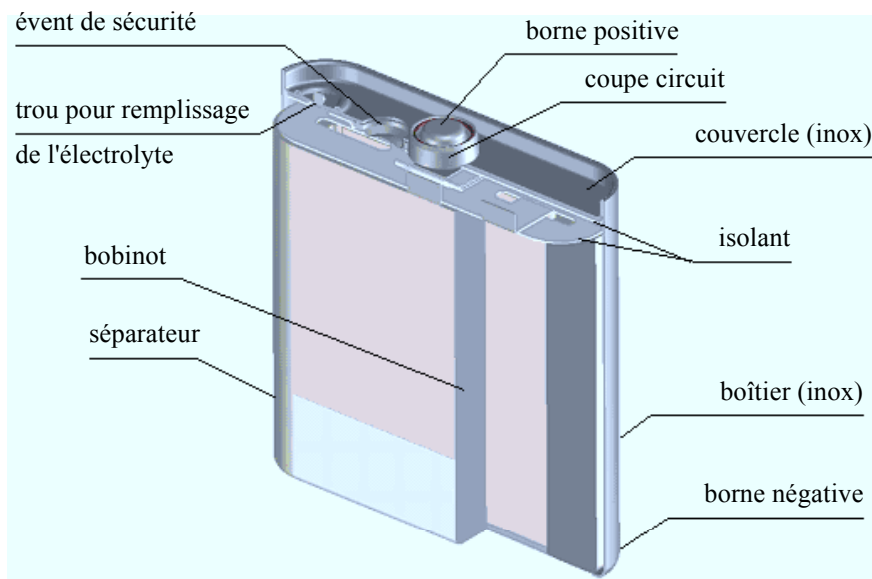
Vue éclatée d'un élément MP 176065 de la société Saft [9]
